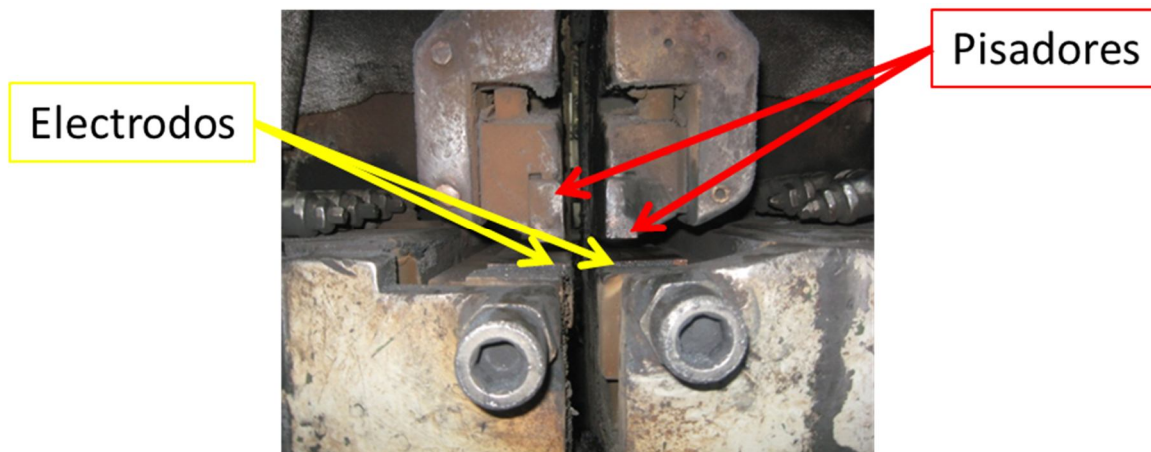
Soldador Swift-Ohio. Detalle de los pisadores y los electrodos.
